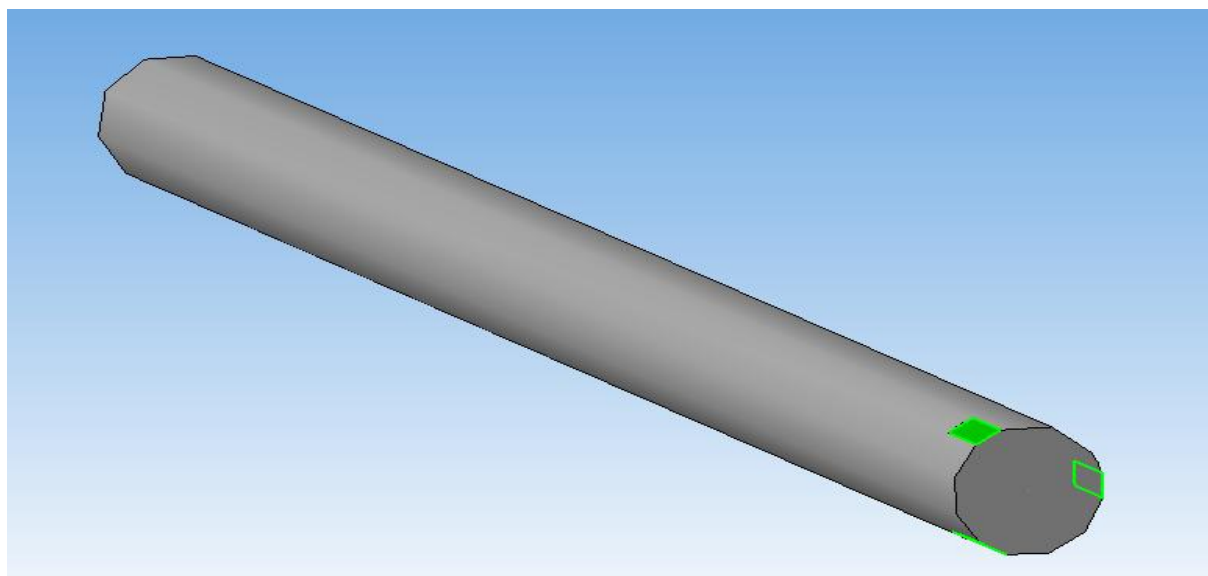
Поверхности (места) закрепления заготовки
